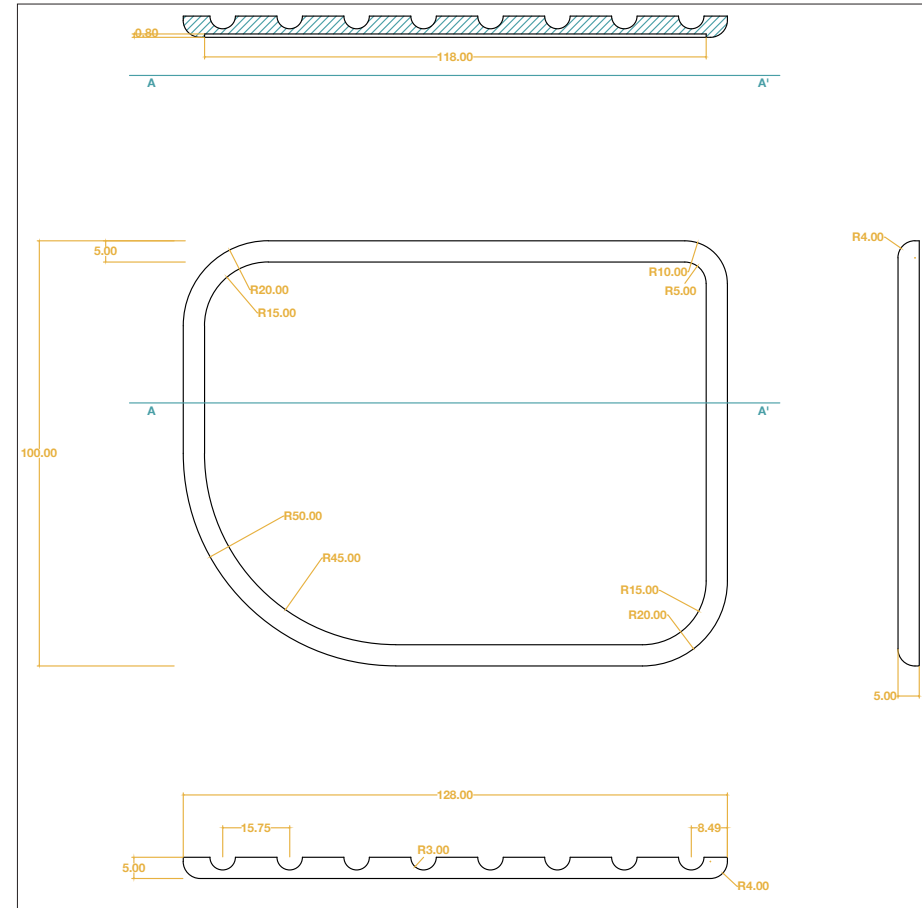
Planta, alzado, perfil y sección de la Pantalla A.
